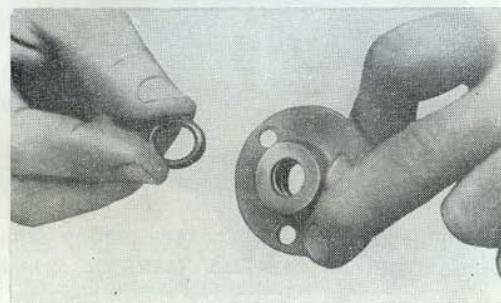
Установка уплотнительного кольца крышки вала переключения
